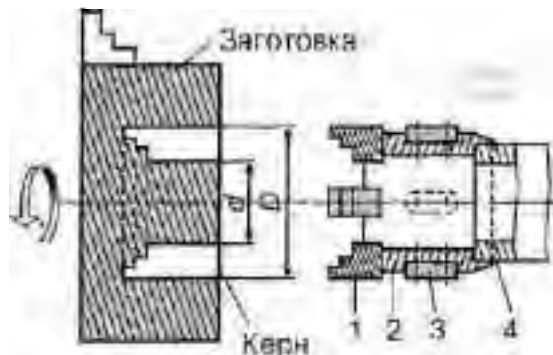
СВЕРДЛО ДЛЯ КІЛЬЦЕВОГО СВЕРДЛІННЯ
